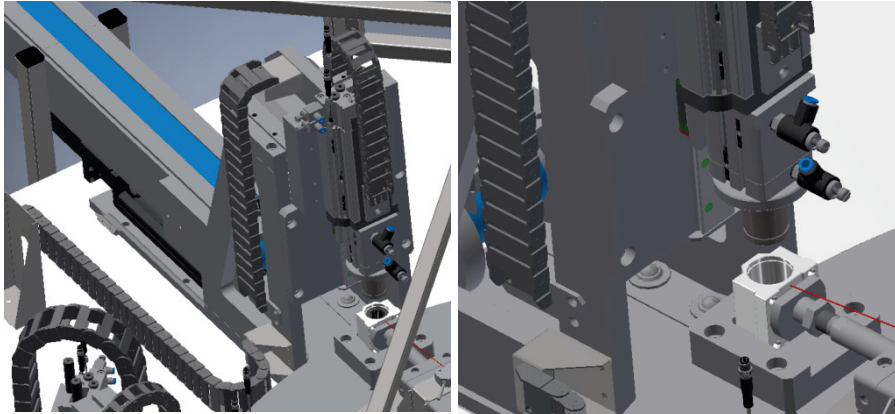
Widok prasy pierścienia zabezpieczającego
